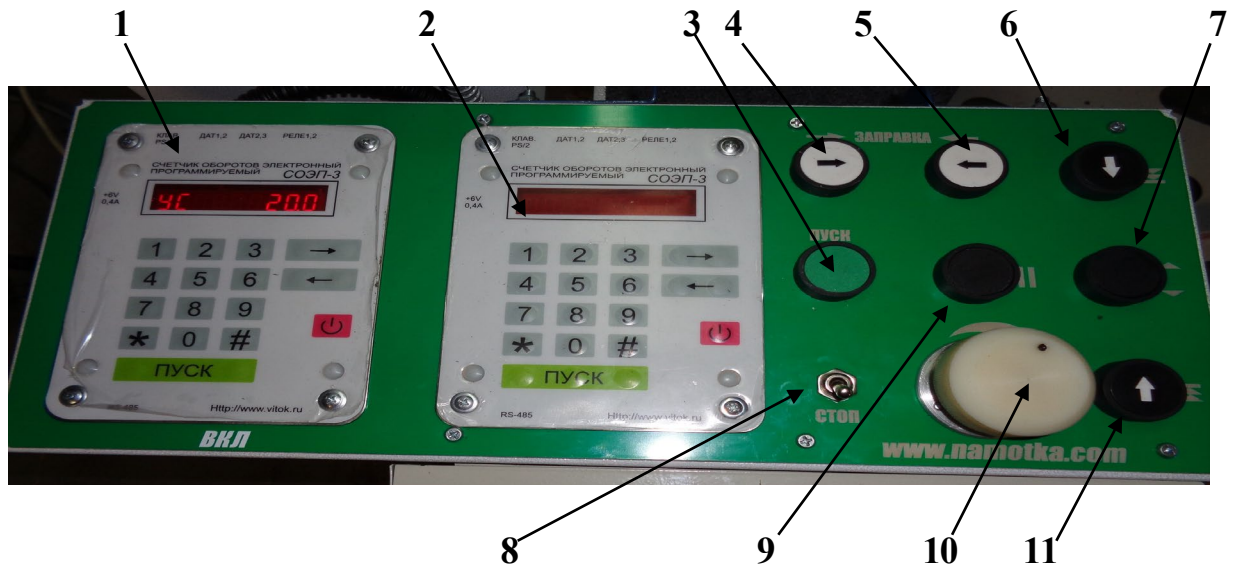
Блок управления станка СН-60-800 ПТ
